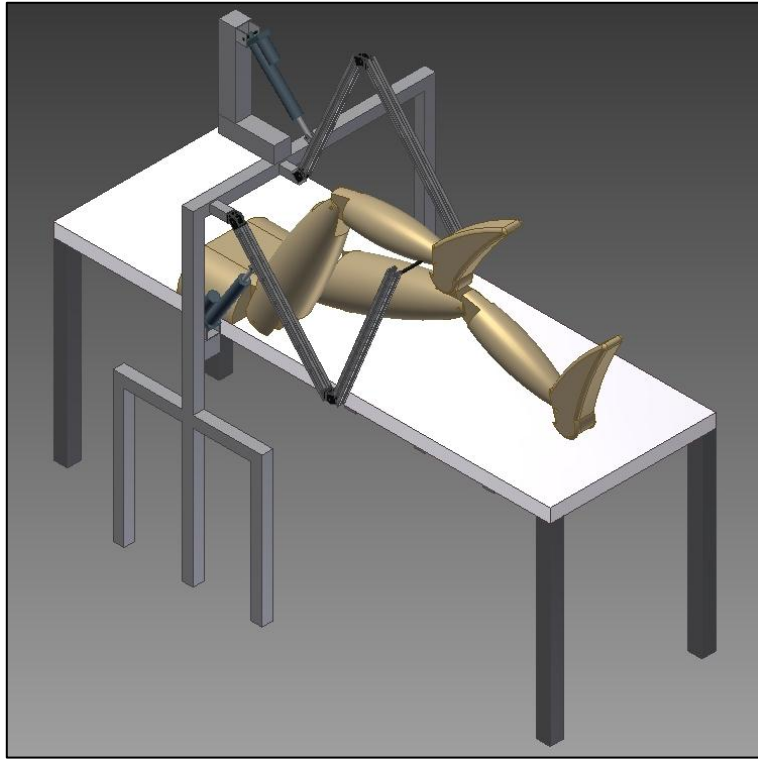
Dibujo CAD del mecanismo sujetando la pierna del paciente. Vista desde esquina.
